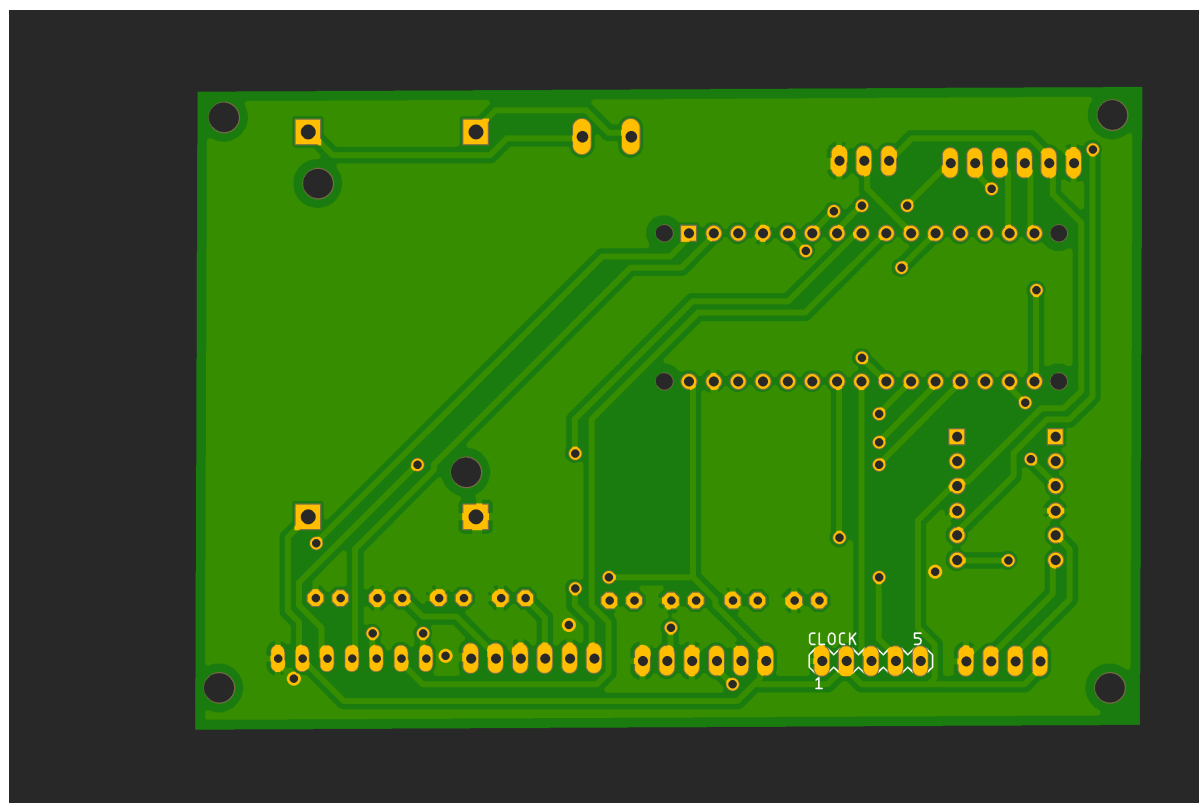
Capa superior PCB modo manufactura.(Autor)
